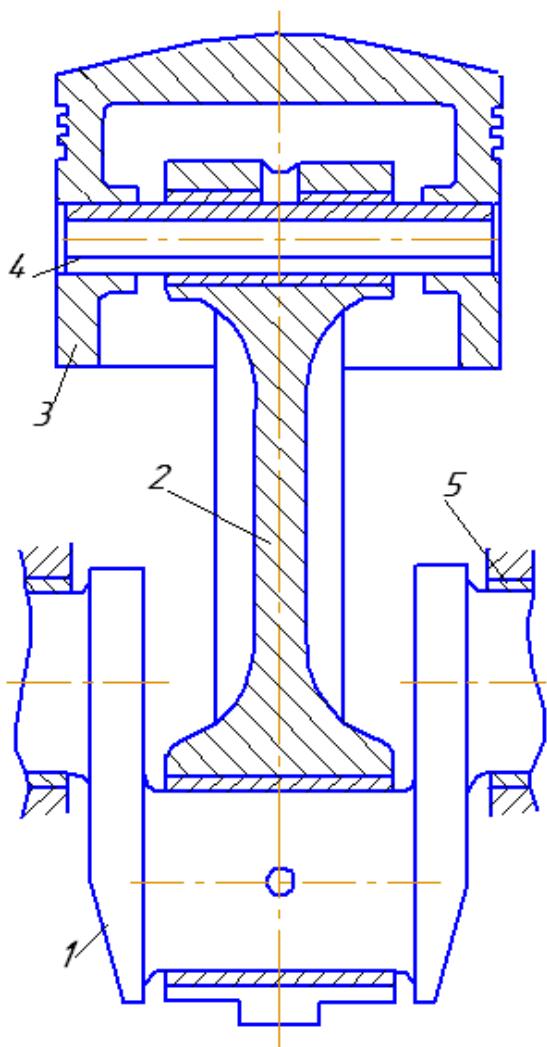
Кривошипно-поршневой узел двигателя
